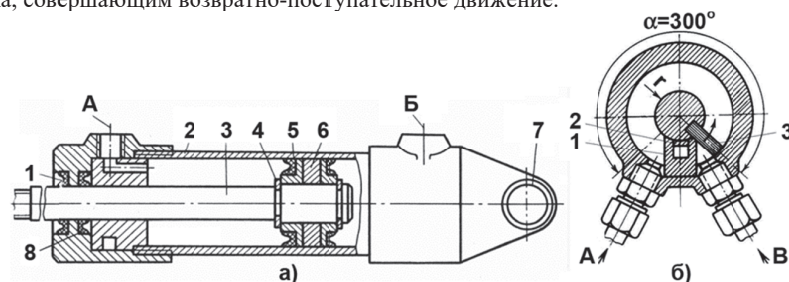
Гидроцилиндр двустороннего действия (а); поворотный двигатель (б)
